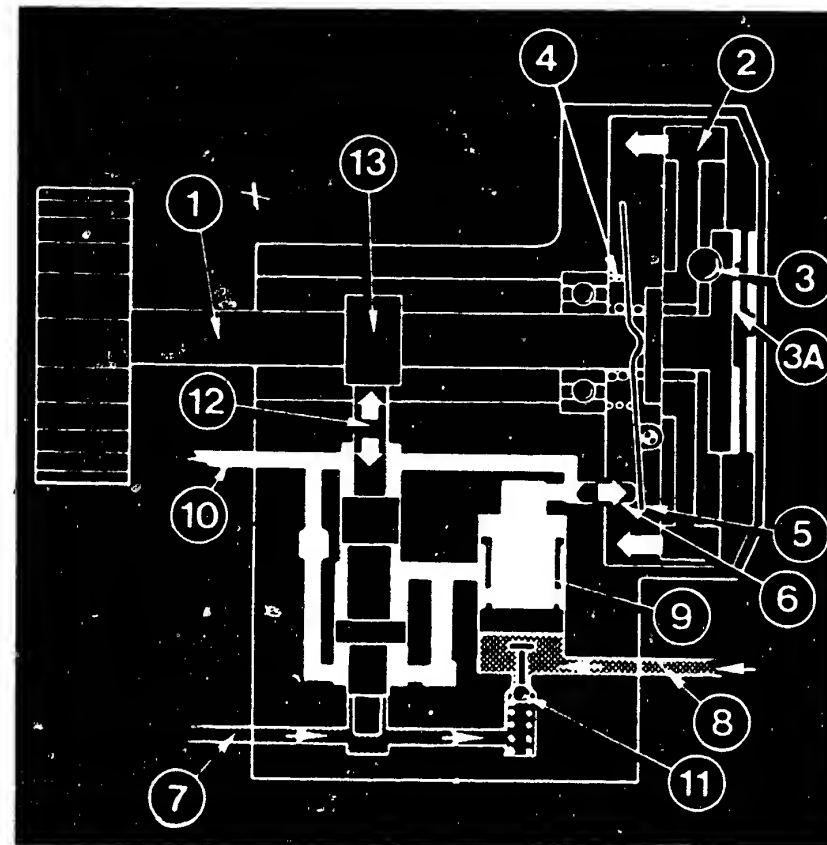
Funktionszustand des Modulators: Druckabbau. Feiner Raster (7) Hauptzylinderdruck, schwacher Raster = drucklos, grober Raster = Radzylinderdruck. Legende wie Bild 3. 13 = Exzenter.
